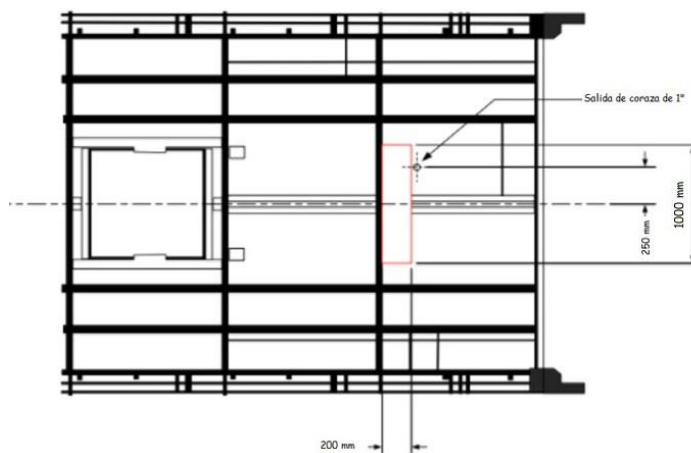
Refuerzo en carrocería para panel para información al pasajero
